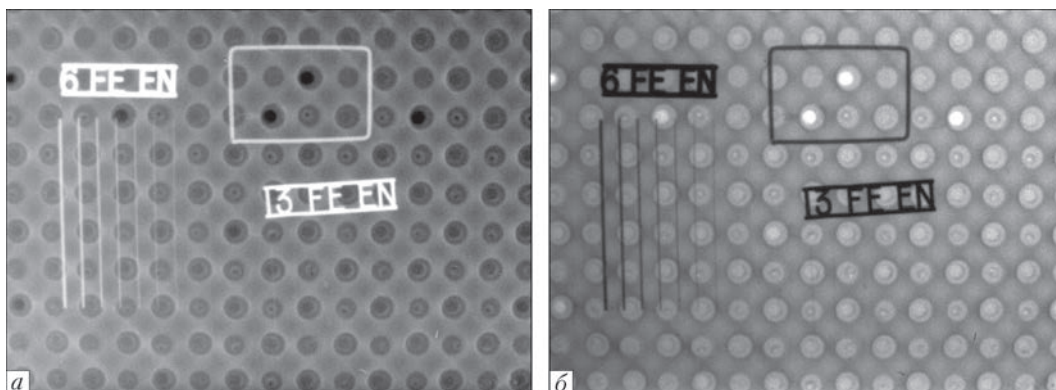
Цифровые изображения образца с двойной точечной сваркой с локализацией участка для исследования с помощью твердотельного преобразователя S10811-11: *а* – негатив; *б* – позитив
